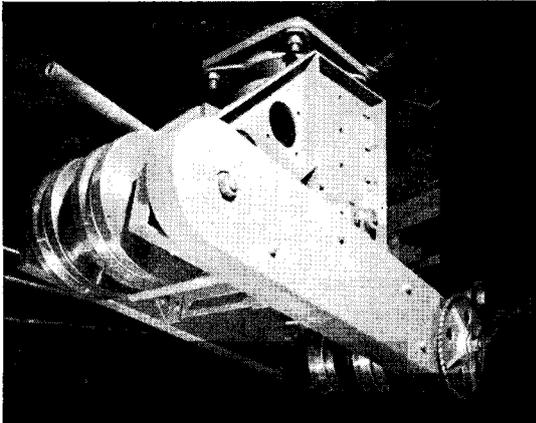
Magnetrollenständer zur Rohrausziehmaschine
